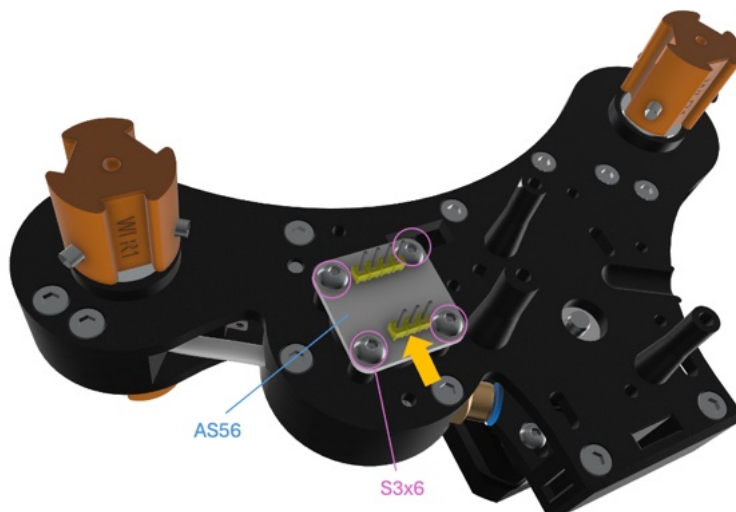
Rewinder-Chassis Montageschritt 25.
